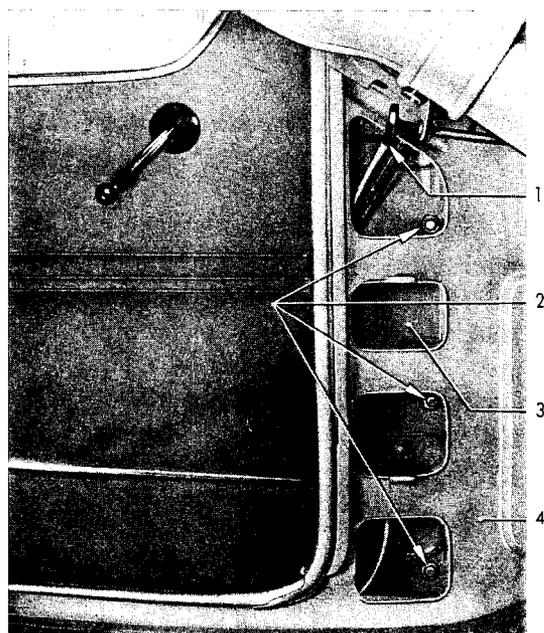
Kotflügelbefestigungsschrauben im Hohlraum der Türscharniersäule
